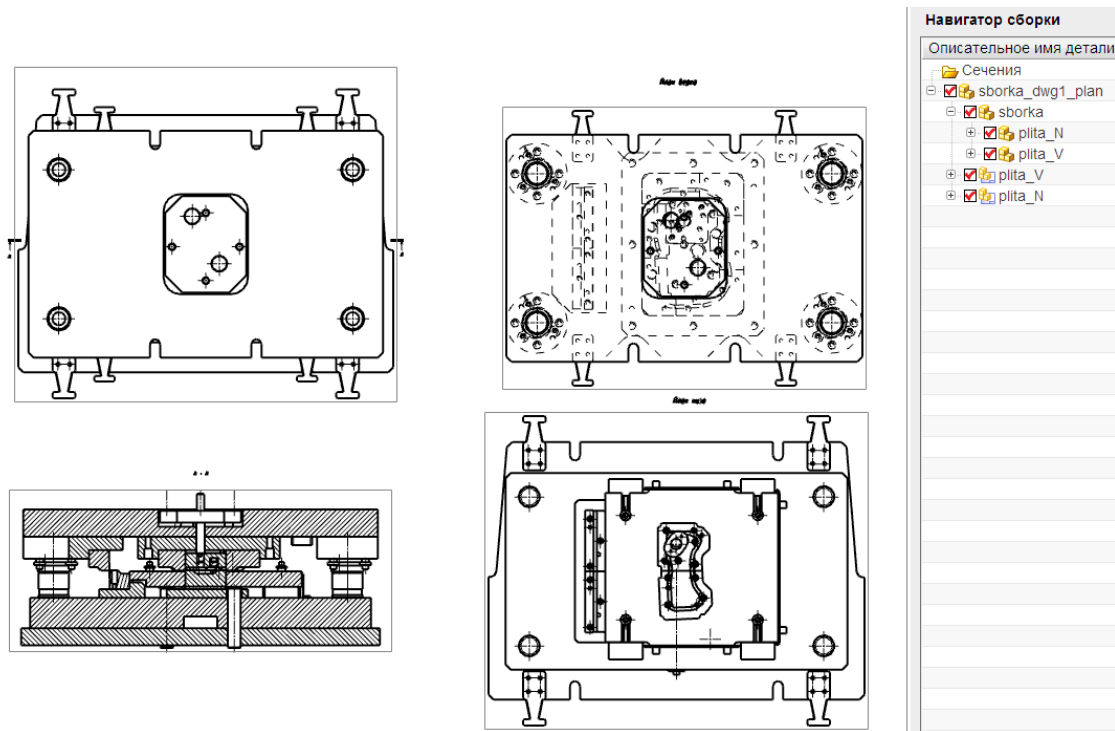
Базовый вид (сверху); сечение базового вида А—А;
